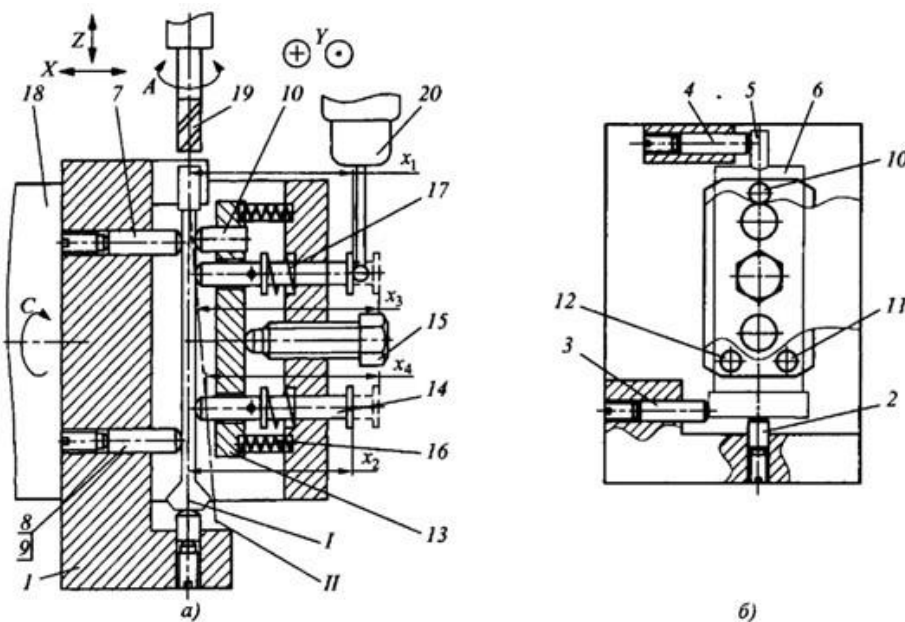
Схема пристрою для виготовлення технологічних баз
